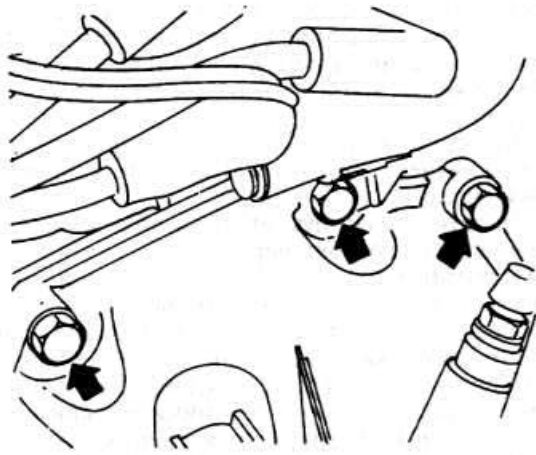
Три верхних болта крепления двигатель/коробка передач
